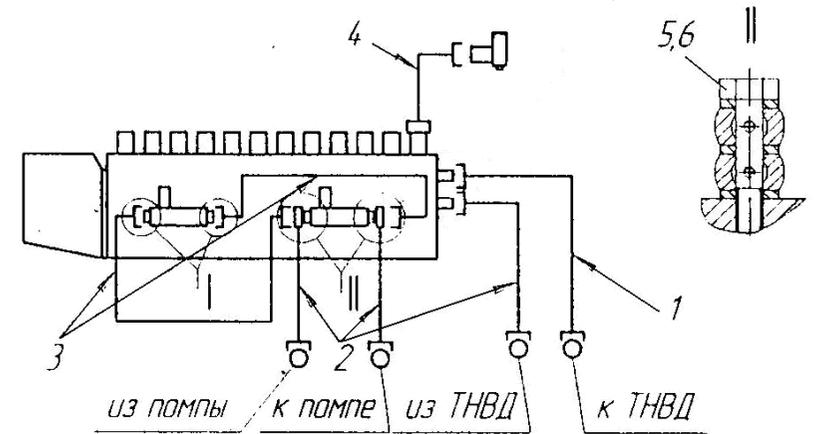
Схема соединения топливопроводов при испытании ТНВД двигателя ЯМЗ-740 со штатным топливоподкачивающим насосом:
